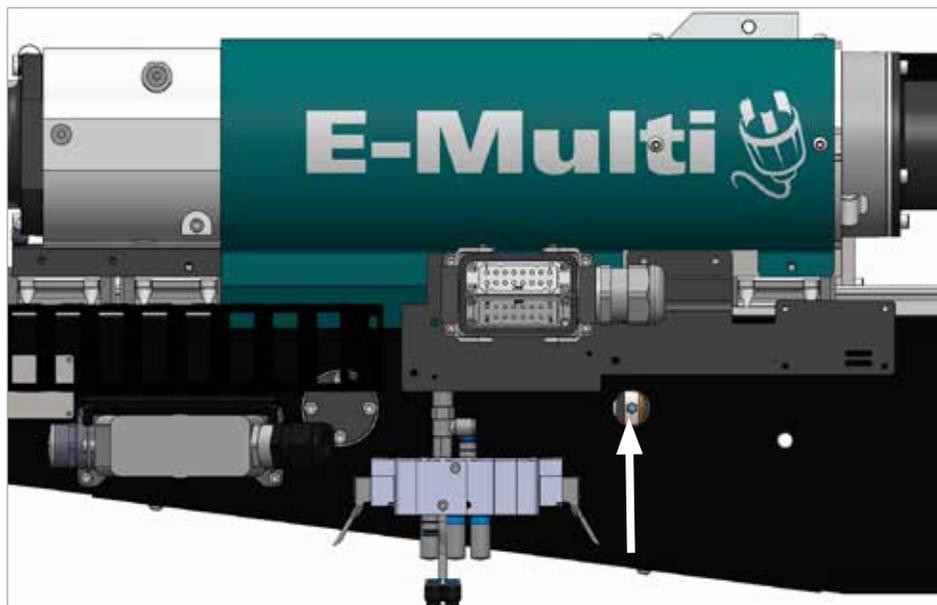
Seitenansicht, die die Position der Schmierpunkte der Kugelgewindespindel des Schlittens zeigt (Systeme aus Mitte 2023 oder später)
